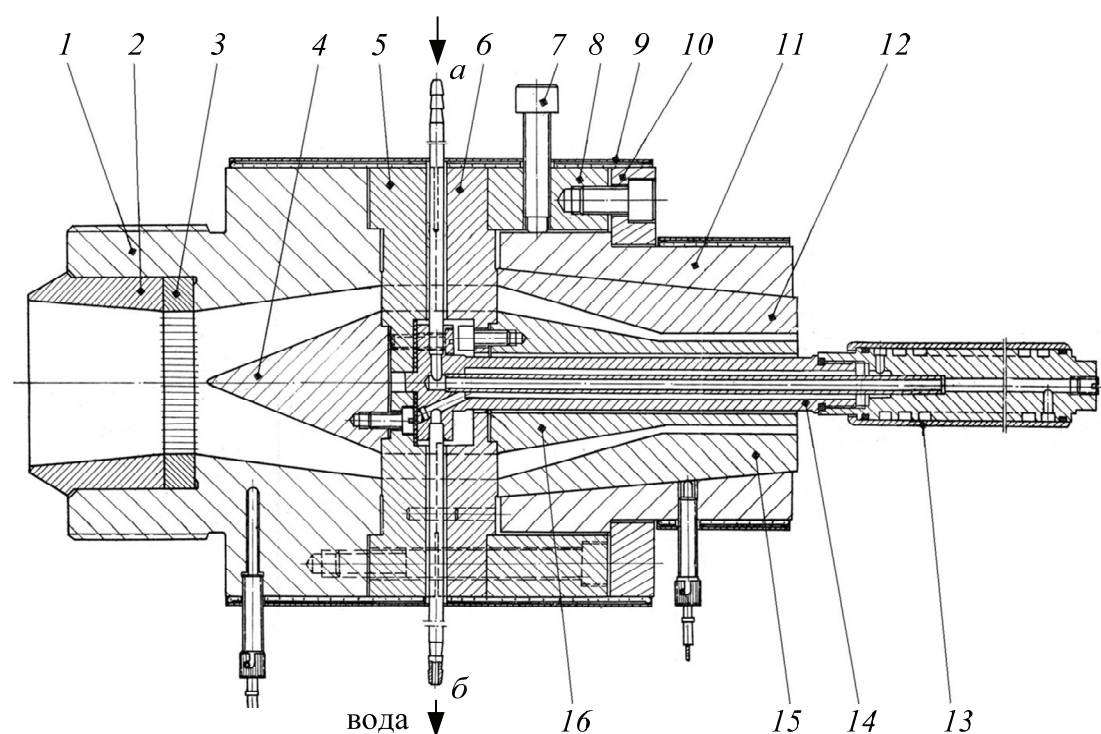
Головка для изделий закрытого типа с калибровкой по внутреннему диаметру:
